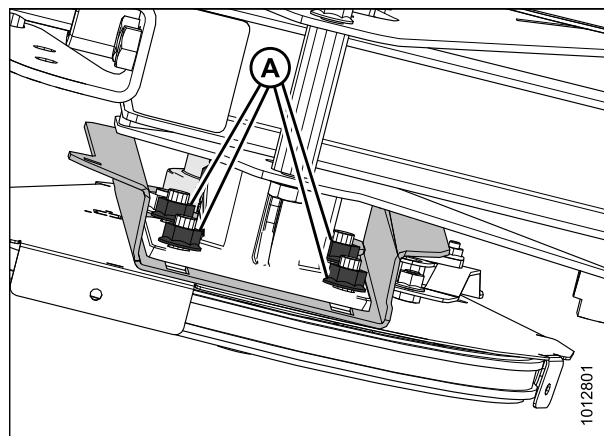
Привод одинарного мотовила — вид из-под низа мотовила
